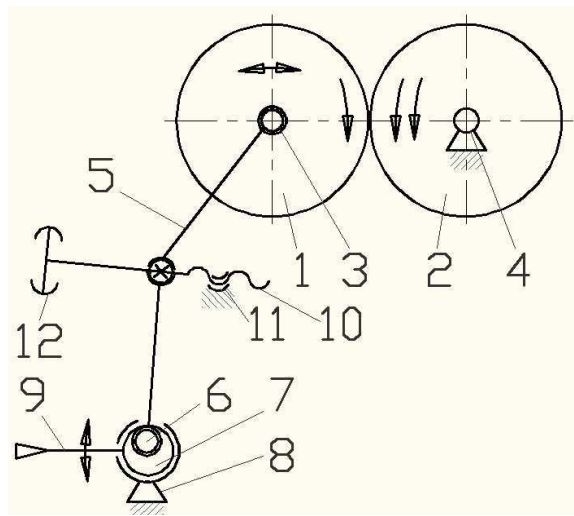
Конструкция установочного механизма с эксцентриковым валом
